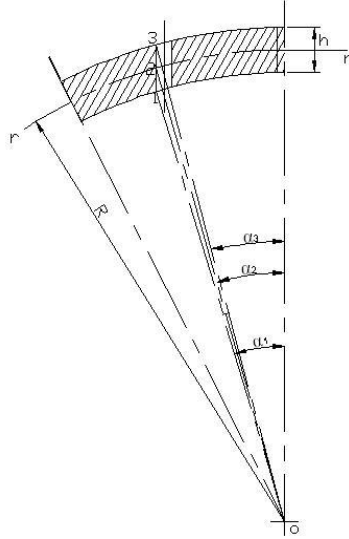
Vista del Plano circular de una Placa con Orificios Verticales.
